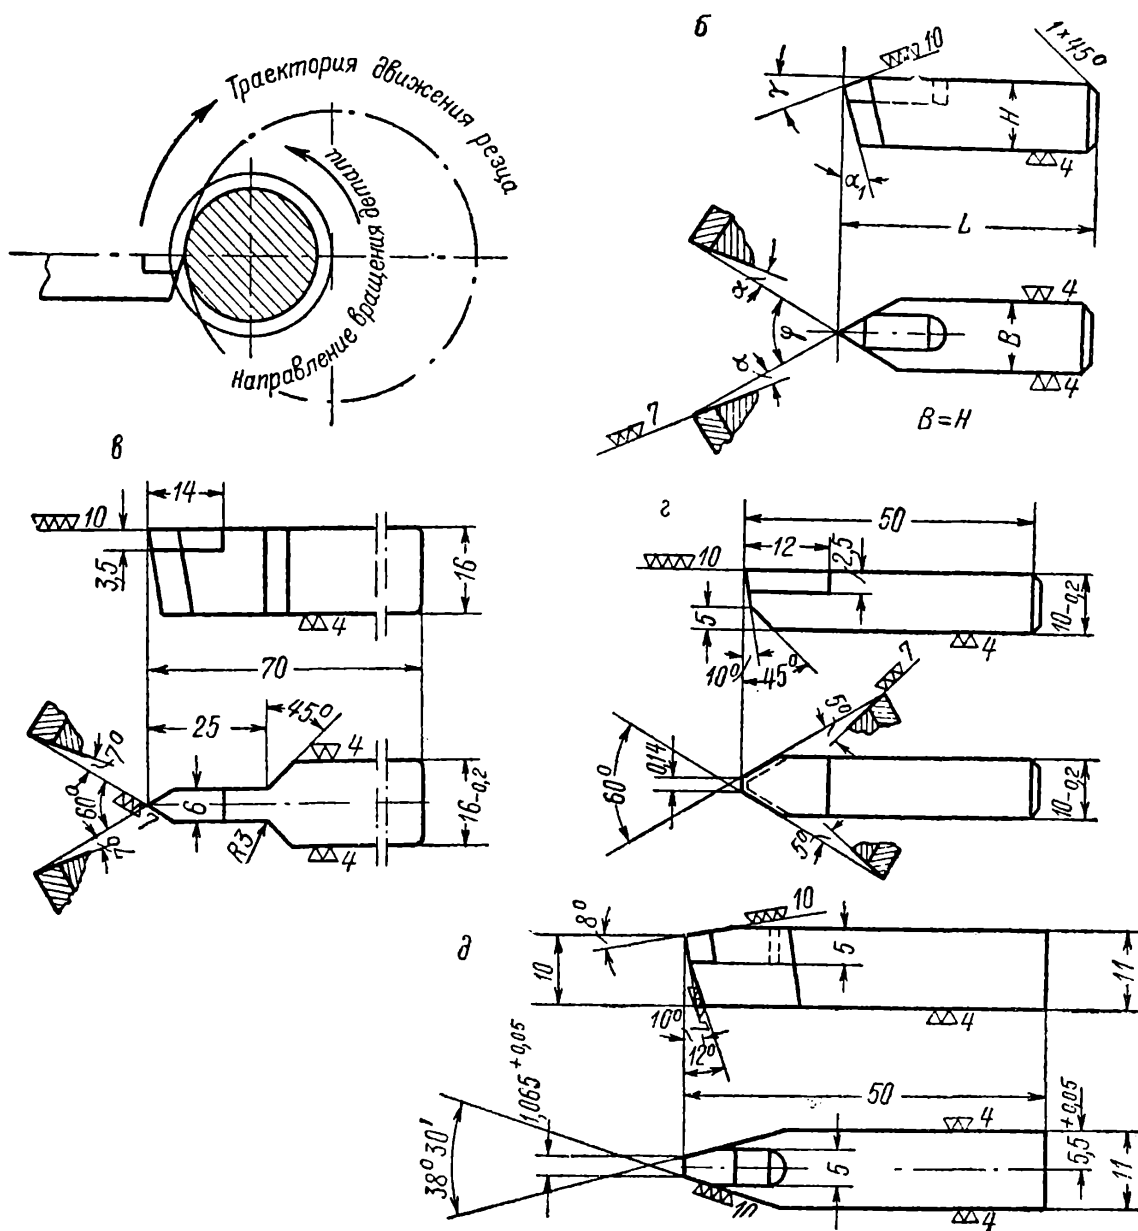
Резьбовые резцы конструкции В. М. Бирюкова.
